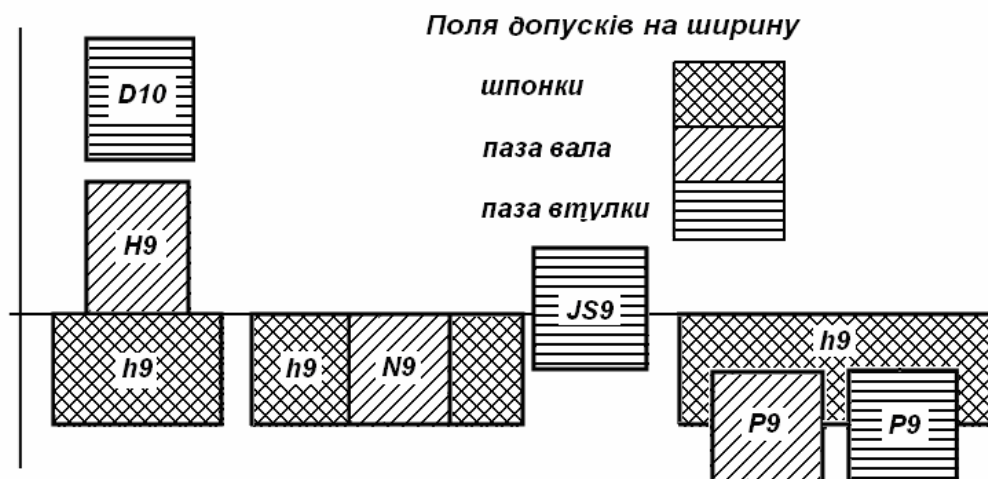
Розташування рекомендованих полів допусків шпонкового з'єднання.
